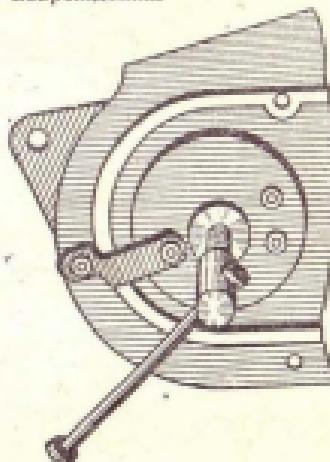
Выпрессовка коленчатого вала из левой половинки картера с помощью съемника и вспомогательной пластины.
